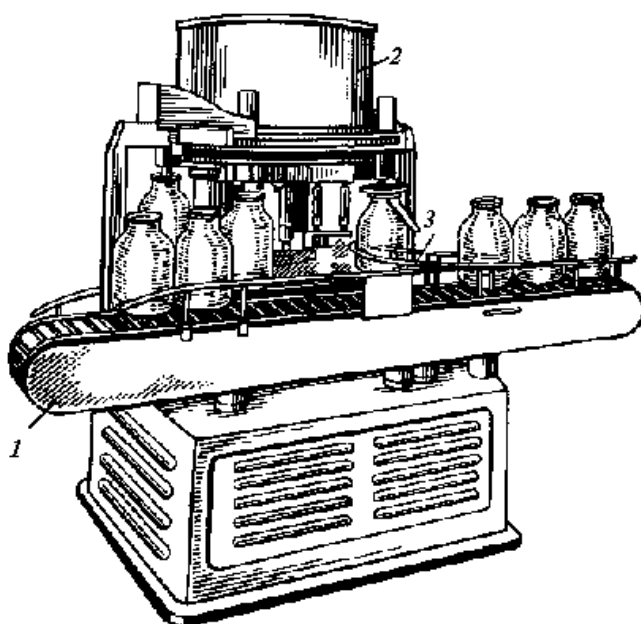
Автоматический наполнитель ДНЗ-3-63: 1- транспортер; 2 - бак; 3 - стол
